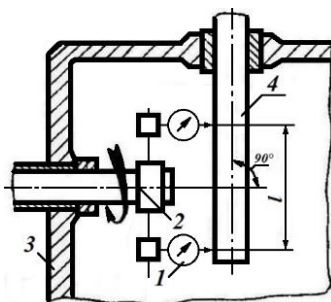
Схема контроля перпендикулярности осей отверстий в корпусных деталях
